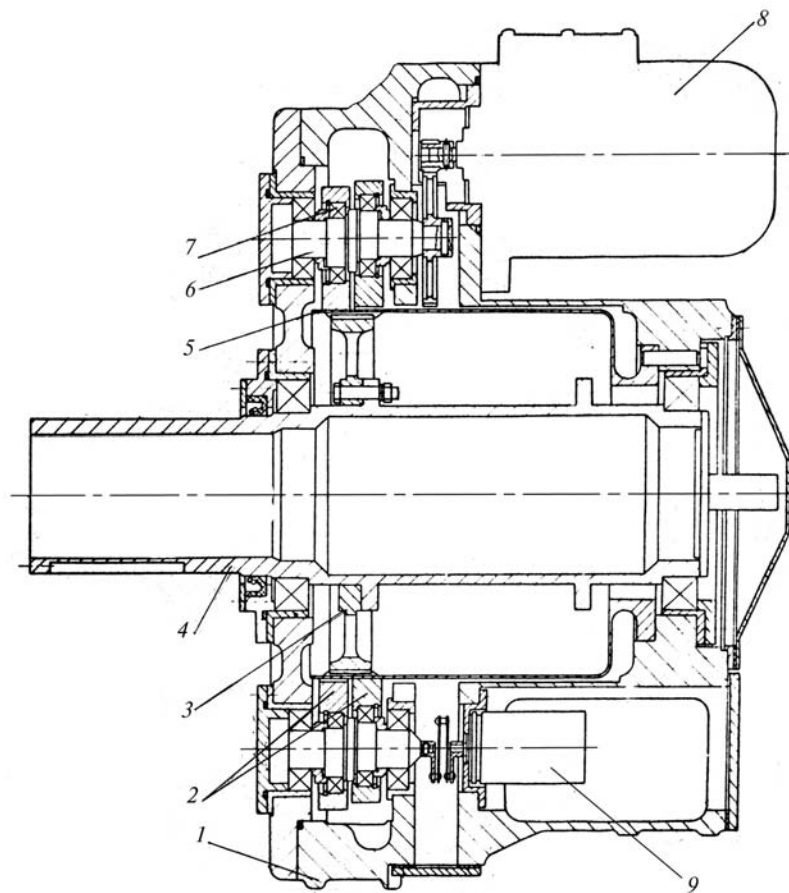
Волновой зубчатый редуктор внешнего деформирования
